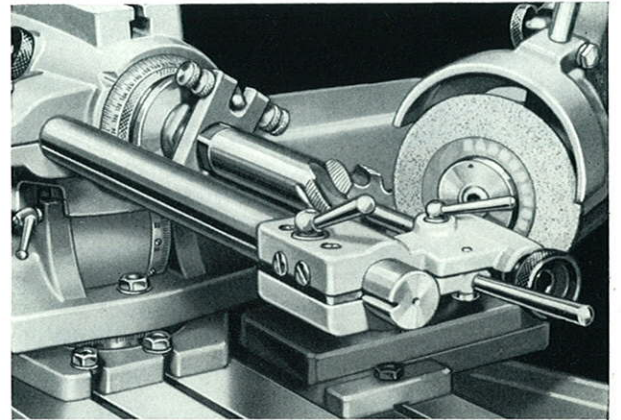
Schleifen des Gewindeanschnittes eines Gewindebohrers
